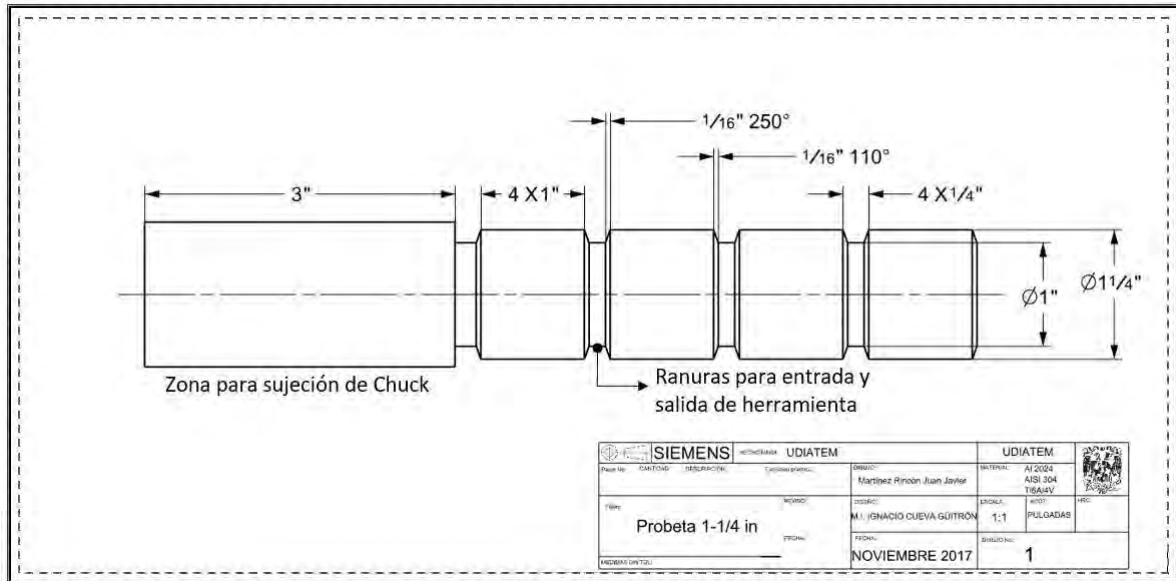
Dibujo técnico de probeta de 1-1/4 in.
